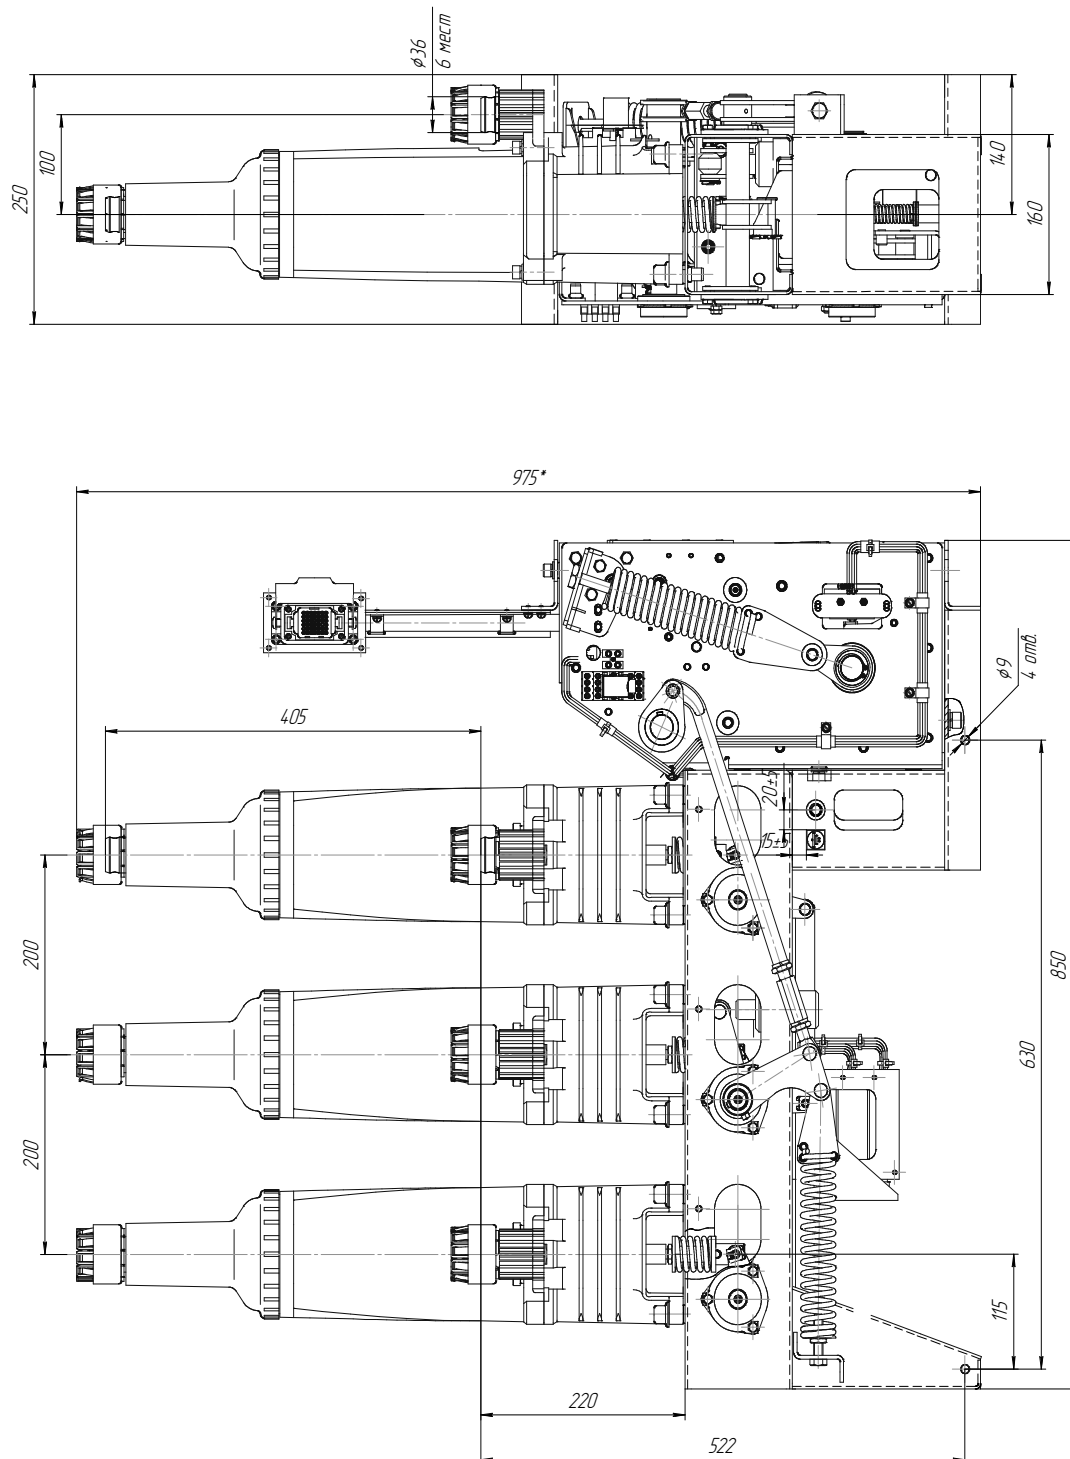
Габаритные, присоединительные и установочные размеры ВВУ-СЭЩ-П4-10-20/1000(1600)
